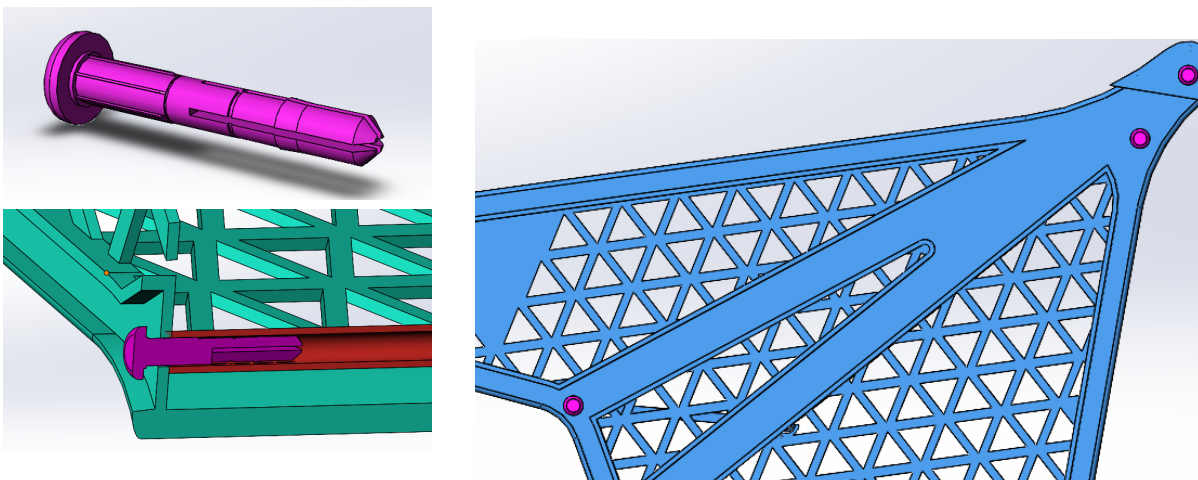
| Tapón de unión y ensamblaje de trampillas
